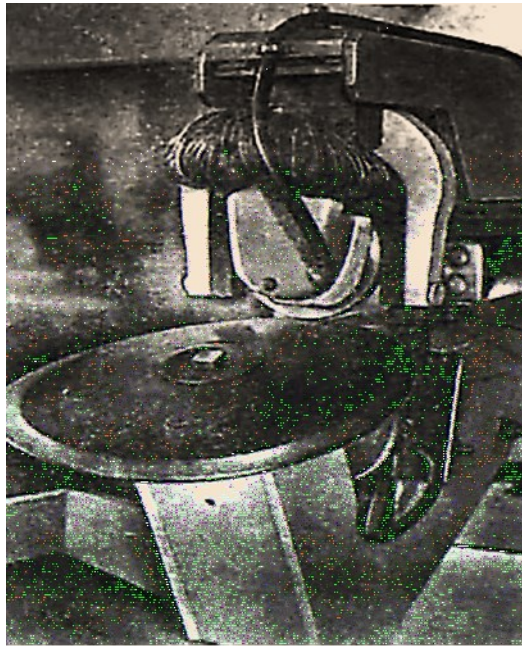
Загальний вигляд установки для приварювання стрічки до диска лущильника на базі модернізованої машини МШПР-300/1200 [1, 3].
